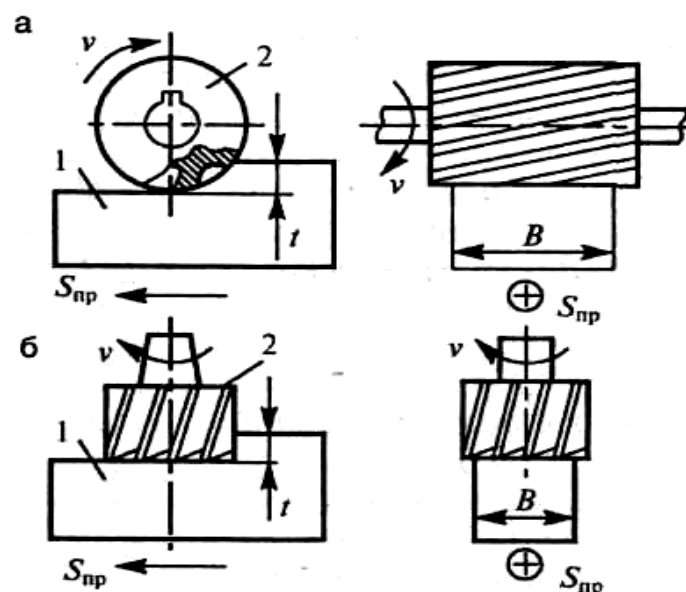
1. Фрезерование фрезами: а – цилиндрической; б – торцевой:
